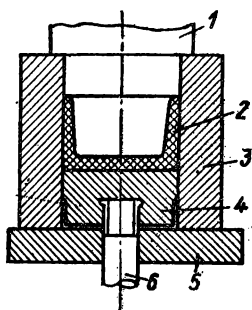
Пример конструкции пресс-формы для компрессионного прессования
